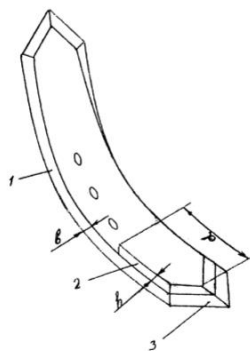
Упрочненное долото глубокорыхлителя (1 - долото , выполненное в виде изогнутой пластины; 2 - наплавленный слой толщиной h и общей длиной d ; 3 - торец рабочей части долота; b - толщина пластины долота)
